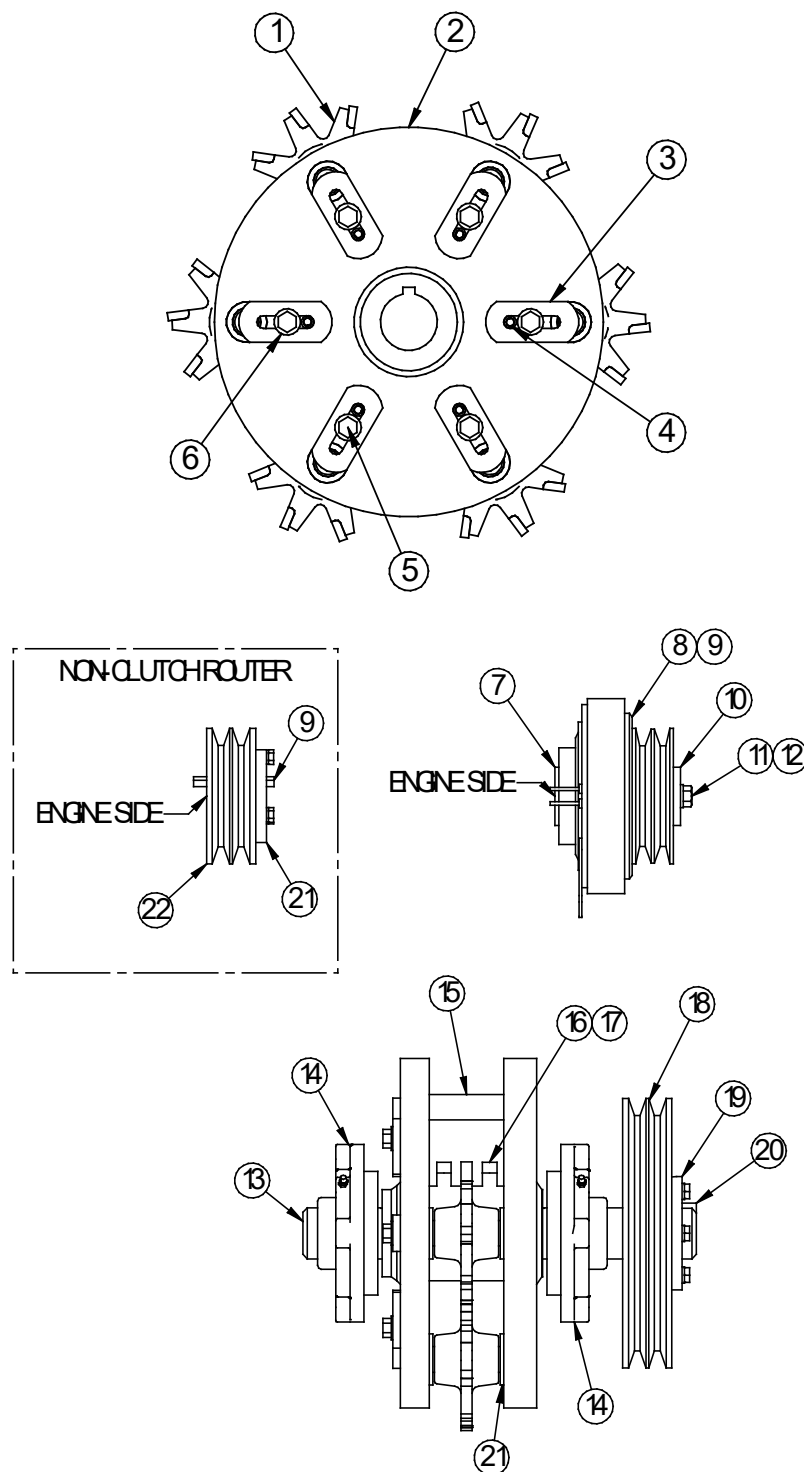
Cabezal de Corte y Ensamble de Transmisión
